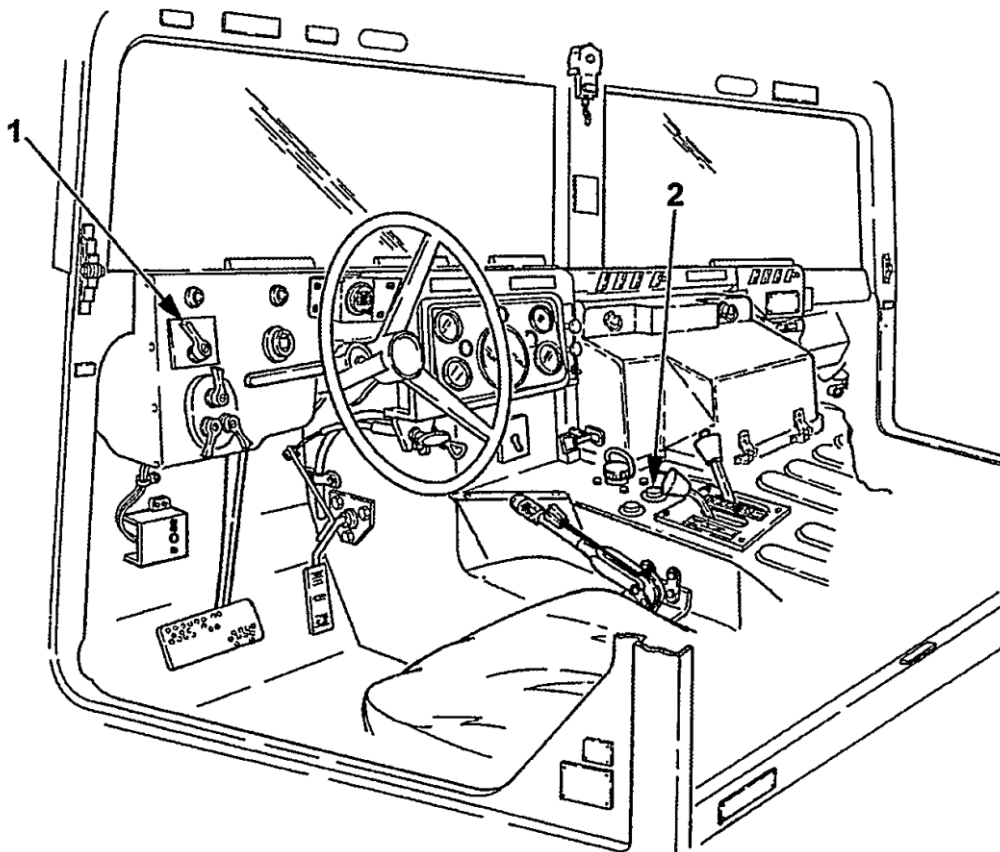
Поворотний перемикач і індикаторний сигнал коробки передач.
